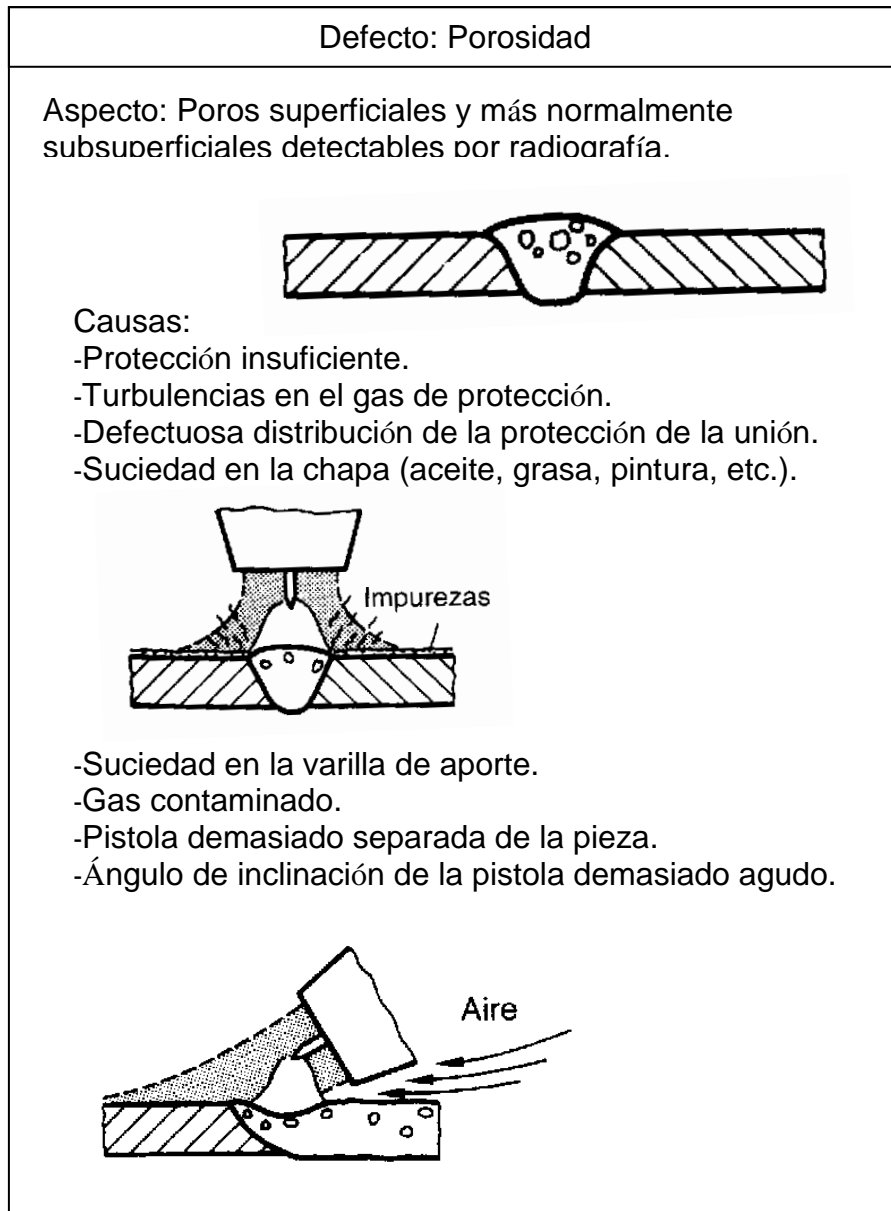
Defecto por porosidad en la soldadura
